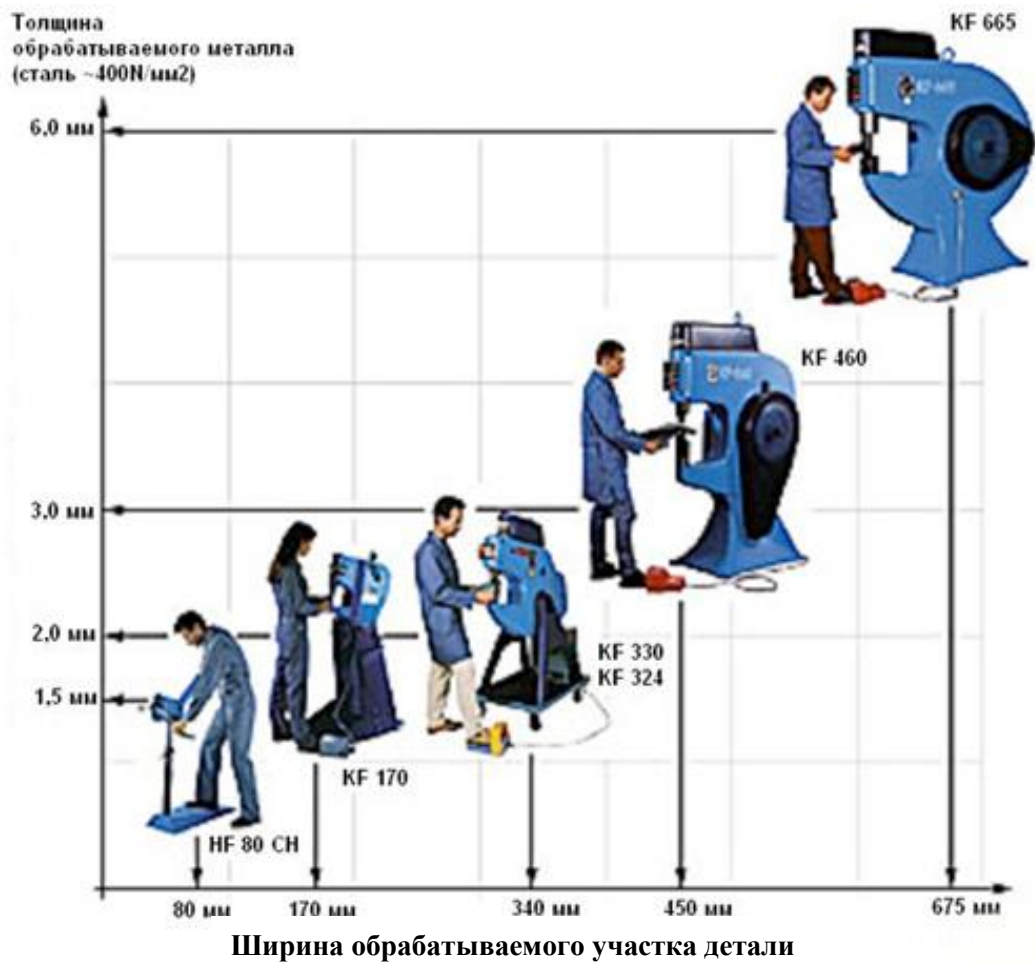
«Линейка» оборудования фирмы Eskold
